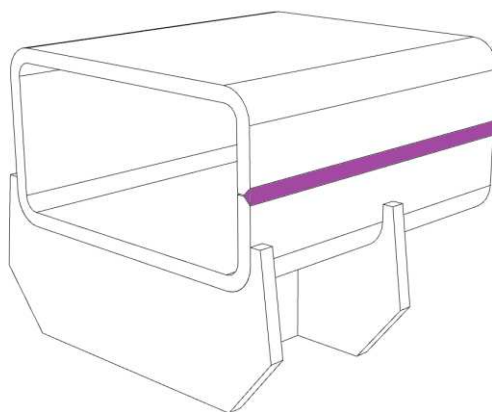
GMI Seiri. Cordón de soldadura del cuerpo.
